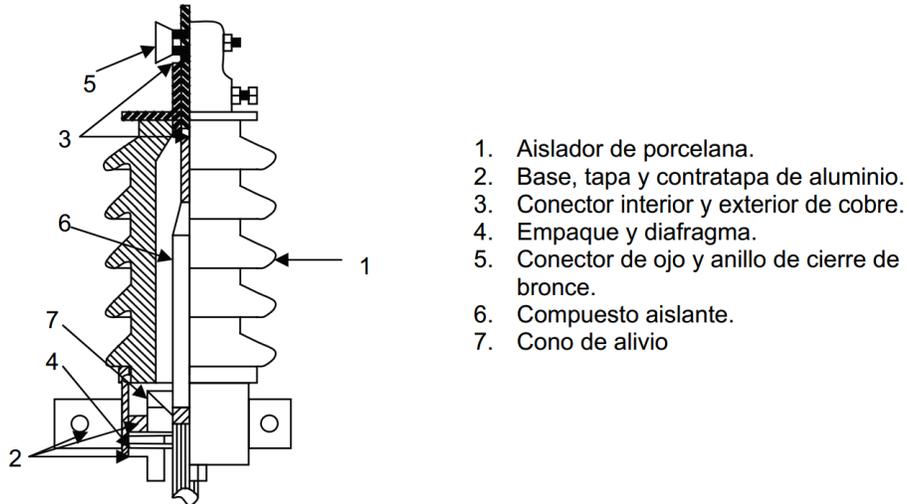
Detalle constructivo de la terminal tipo bayoneta instalada en cable con aislamiento extruido
